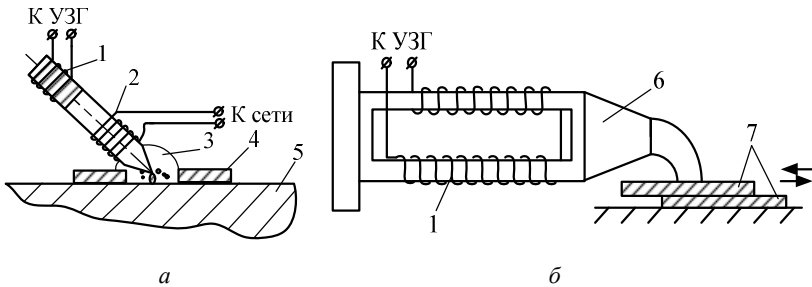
Схемы устройств ультразвуковой пайки (а) и ультразвуковой сварки (б):
